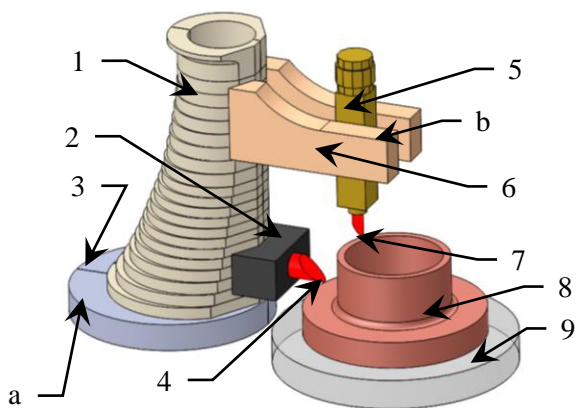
Компонка станка с одной бионической башней ФСД (1); 2 – вертикальный суппорт; 3 – стол башни; 4 – инструмент суппорта; 5 – ползун; 6 – консоль; 7 – инструмент ползуна; 8 – деталь; 9 – планшайба детали; a – прикорневое утолщение башни; b – свес консоли
